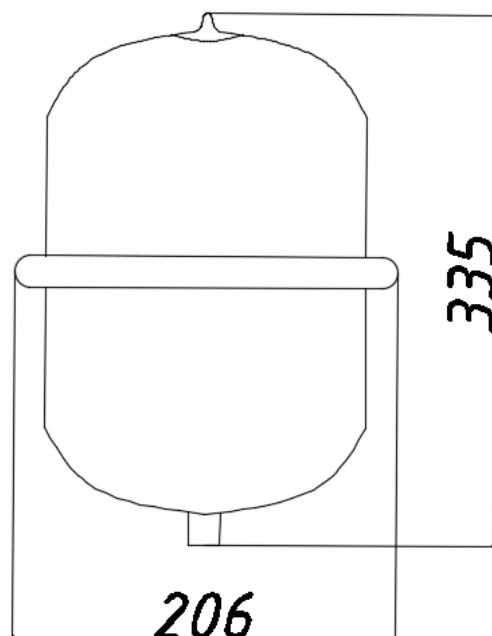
Габаритный чертеж гидробака марки Tank GT-U 8L
